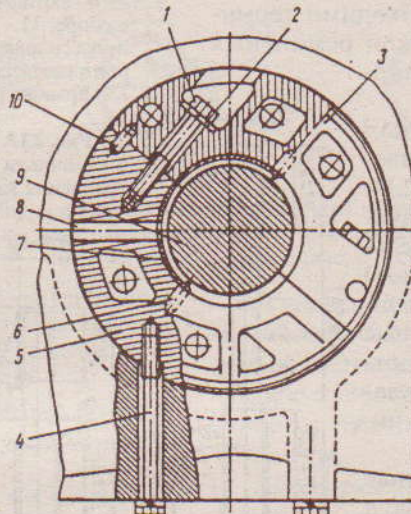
Опора среднего коренного подшипника: 1 - стяжной болт, 2 - шайба; 3 - верхняя опора; 4 - болт крепления средней опоры; 5 - нижняя опора; 6 - штифт вкладыша; 7 - вкладыш; 8 - канал подвода смазки к подшипнику; 9 - коленчатый вал; 10 - штифт опоры
